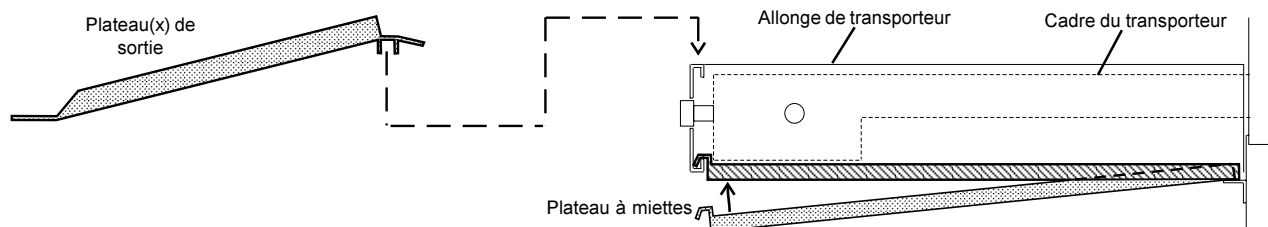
Assemblage final - Plateau(x) de sortie et plateaux à miettes
